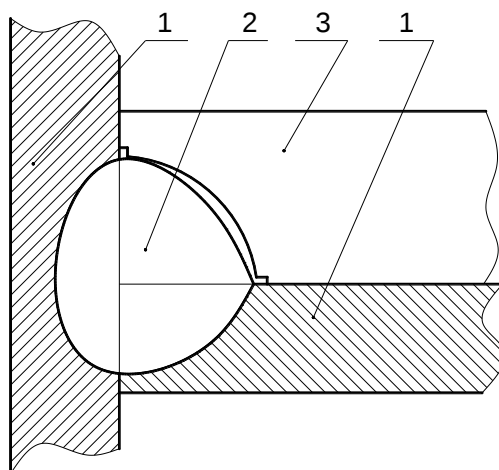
Схема контролю геометричних розмірів зварного шва за допомогою щупа
